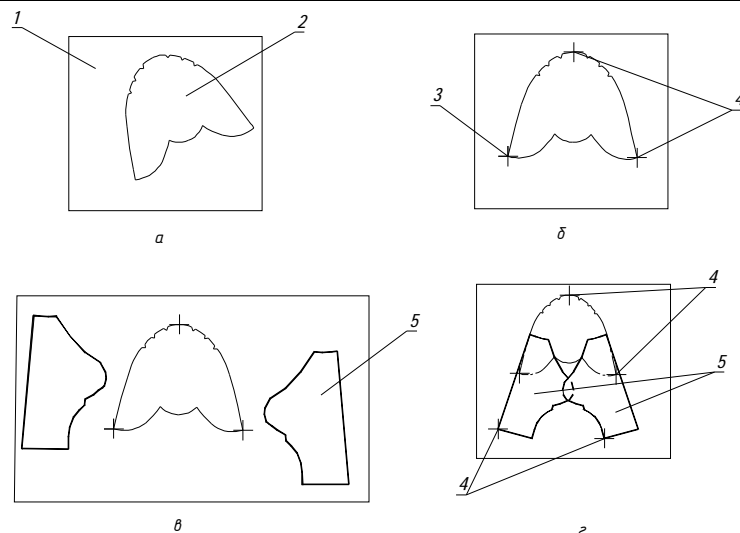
Схема технологічного процесу базування ДВВ: а – завантаження основної деталі; б – базування деталі в базуючих елементах; в – завантаження решти деталей; г – взаємне базування деталей; 1 – основа; 2 – основна деталь; 3 – нерухомий базуючий елемент; 4 – рухомі базуючі елементи; 5 – деталі
